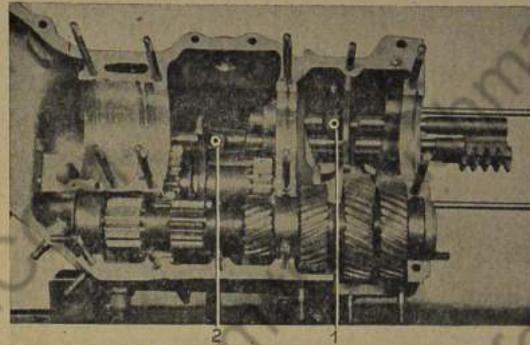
Zentrierschrauben für Schaltgabeln 1.-2. und 3.-4. Gang festziehen
